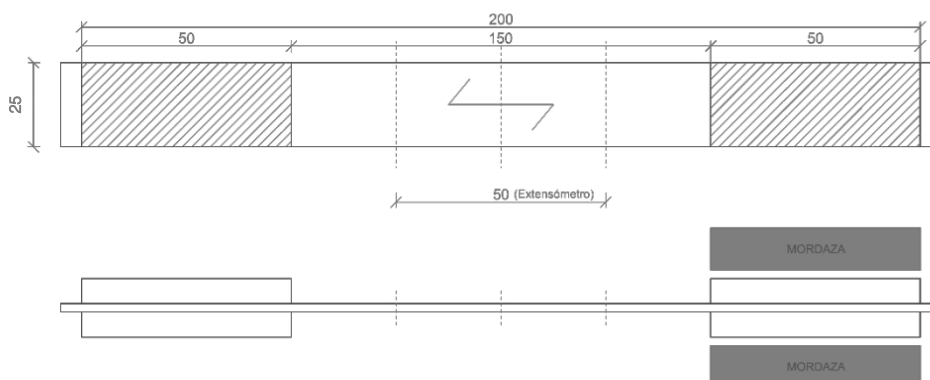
Dimensiones nominales en mm de la probeta ISO 13934-1.
